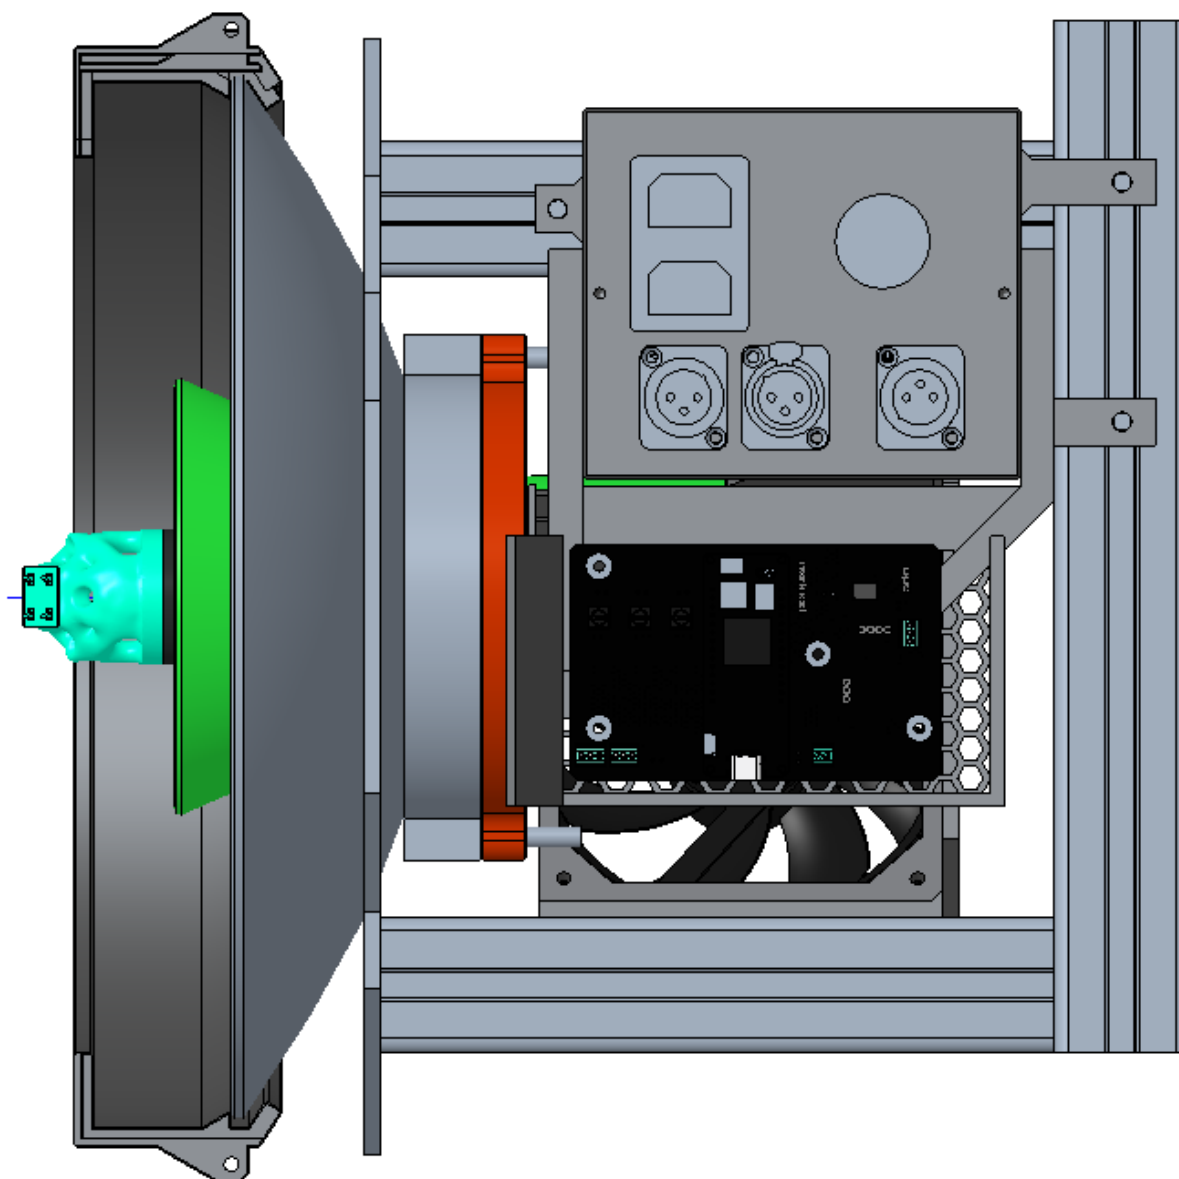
Seitenansicht gesamte Baugruppe: mittig Elektronikgehäuse mit Platine.
